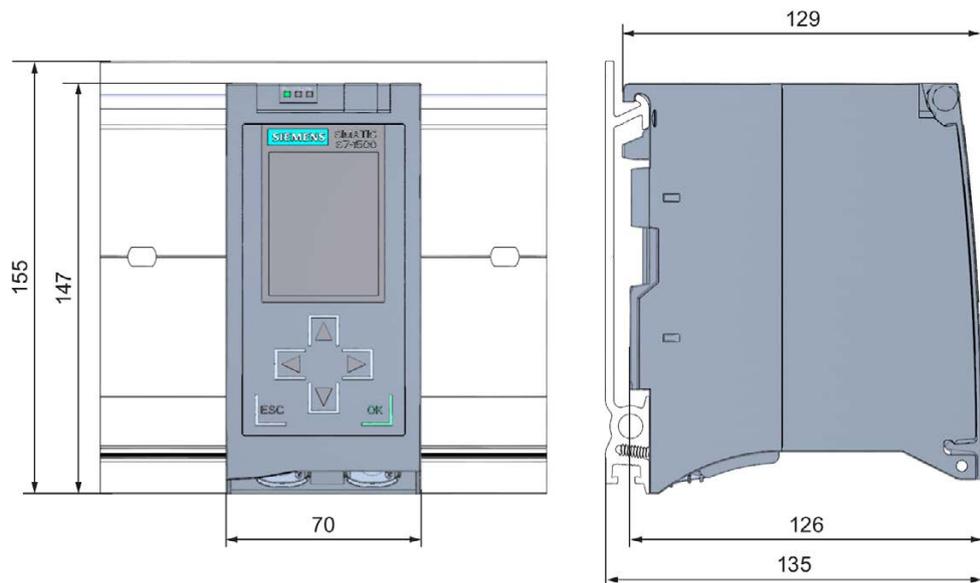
Dessin coté de la CPU 1515-2 PN, vue de face et vue latérale
